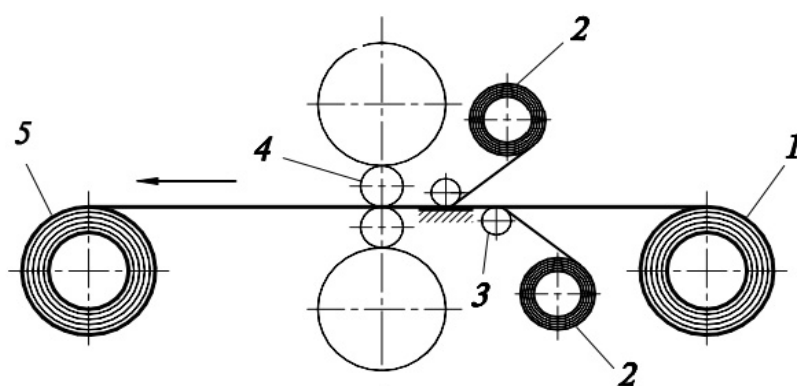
Рулонная прокатка трёхслойного биметалла:
